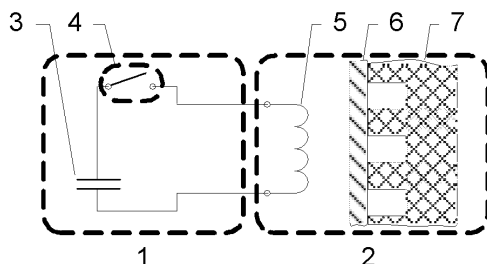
Схема установки магнитно-импульсной штамповки: 1 – высоковольтная система; 2 – индукторная система; 3 – емкостный накопитель энергии; 4 – устройство управления; 5 – индуктор; 6 – листовая заготовка; 7 – матрица
